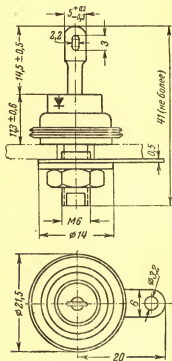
Габаритный чертеж диодов Д231—Д234БП.
